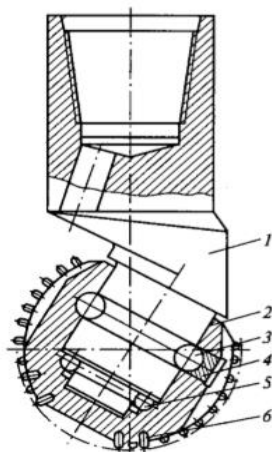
Одношарошечное долото: 1 – лапка; 2 – шарошка; 3,5 – шарики; 4 – палец; 6 – твердосплавленный зубец
